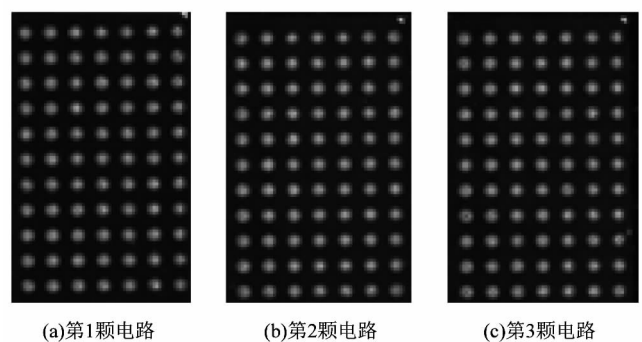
试验前 BGA 电路的焊球表面形貌
